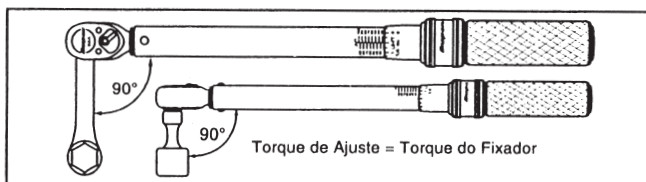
Uso de extensões/universais oscilantes com chaves dinamométricas.
